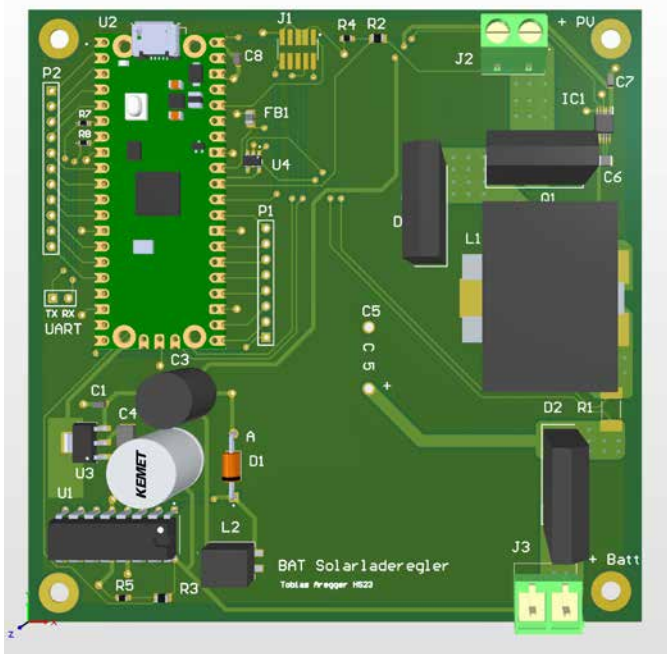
Bestücktes PCB in der 3-D Ansicht in Altium
